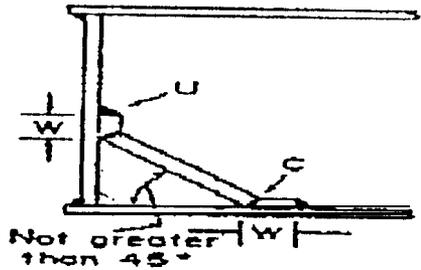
REFUERZOS PARA TAPAS PLANAS (REF.4)
